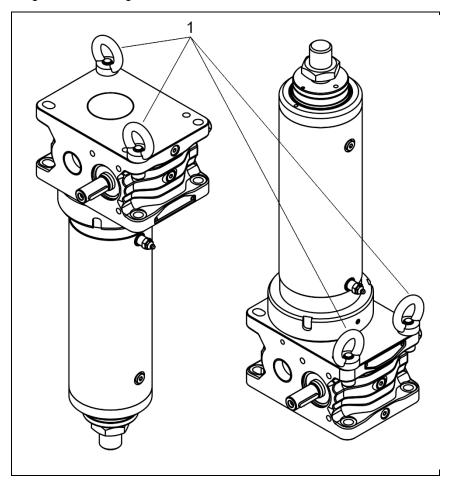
Ringschrauben (1) oder Ringmuttern (nicht im Lieferumfang)
